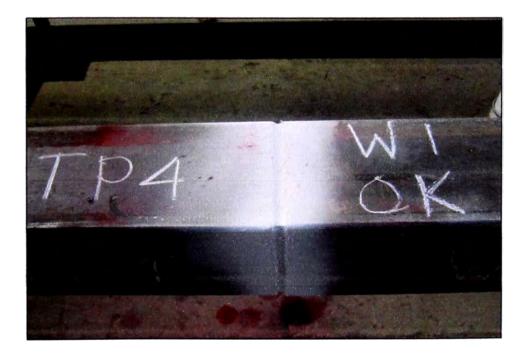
Inspección de pase raíz en amarre pórticos TP-4, soldador w1.
